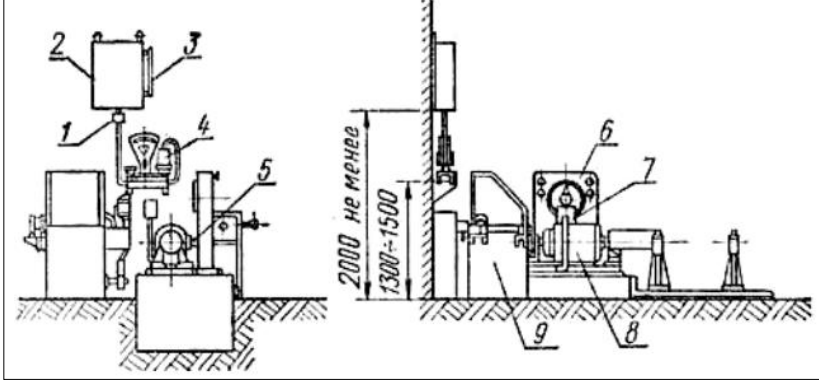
Установа для перевірки бічного зазору у зачепленні циліндричних зубчатих коліс:
